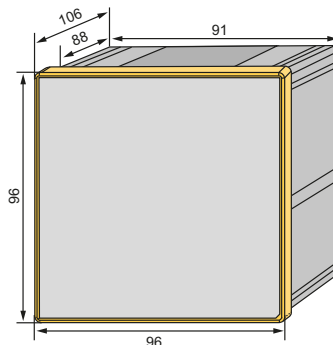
Maßbild PEM575 (Frontansicht)
